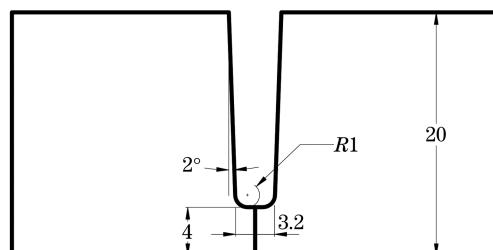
20 mm厚TC4钛合金窄间隙焊接坡口尺寸
